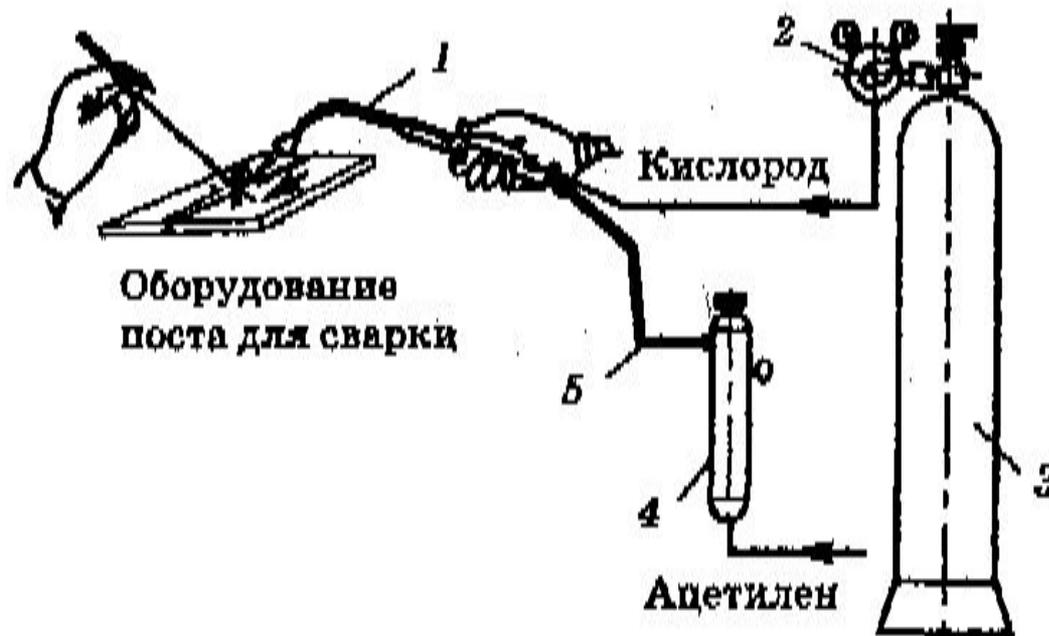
Оборудование поста для газовой сварки:
